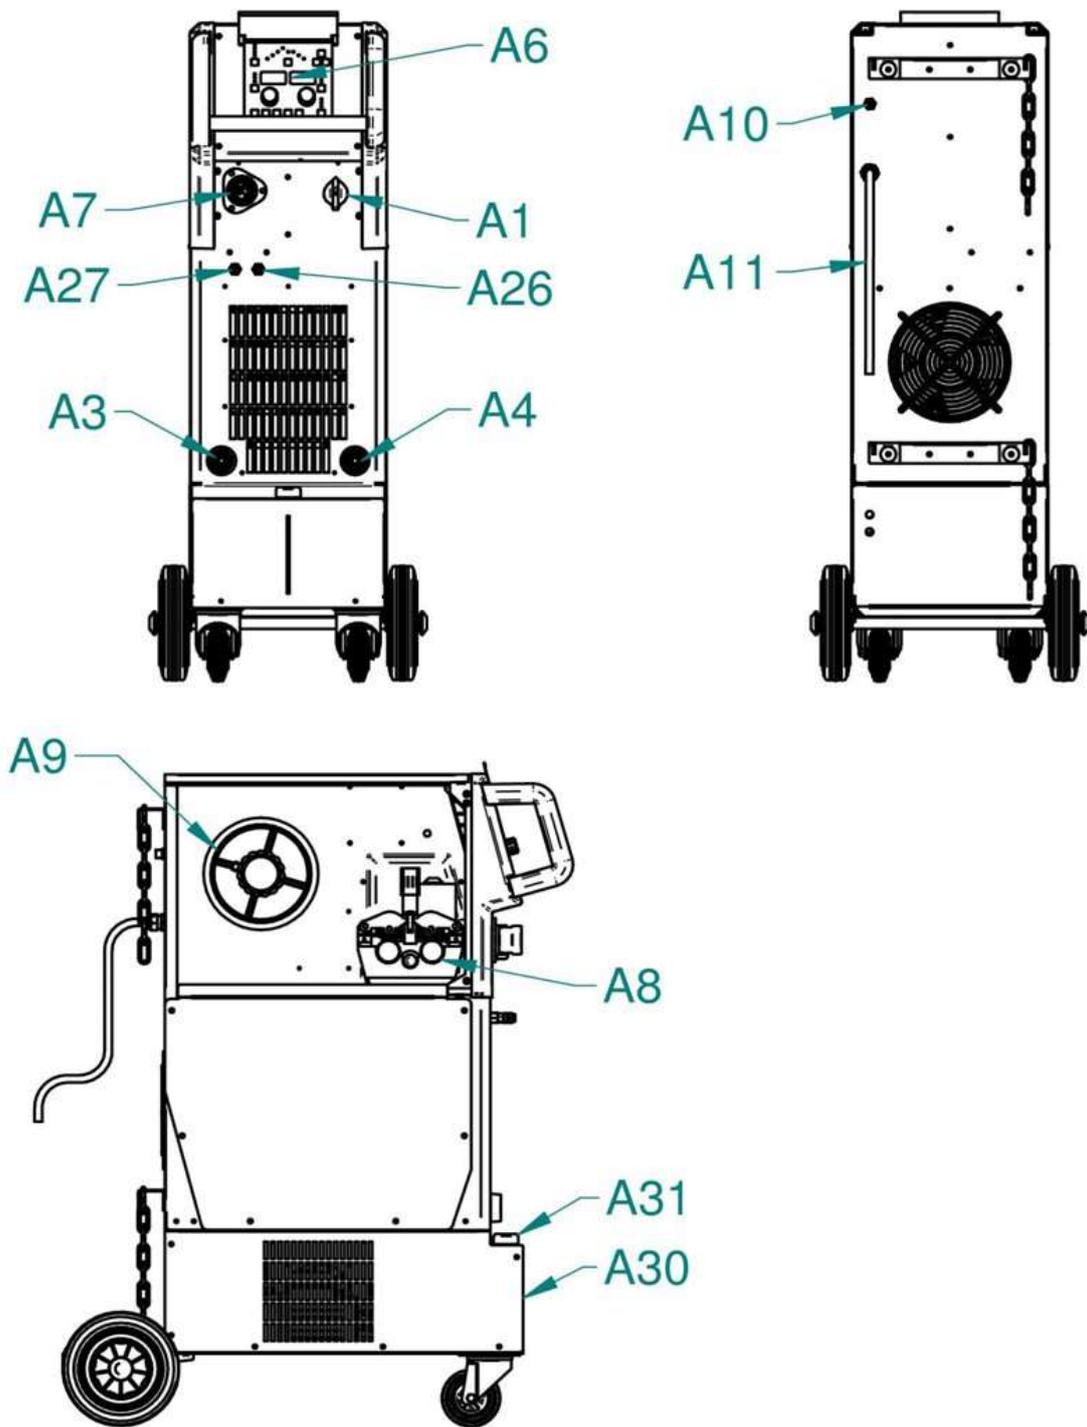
Hauptteile der Maschine aXe 400/500 IN Compact
